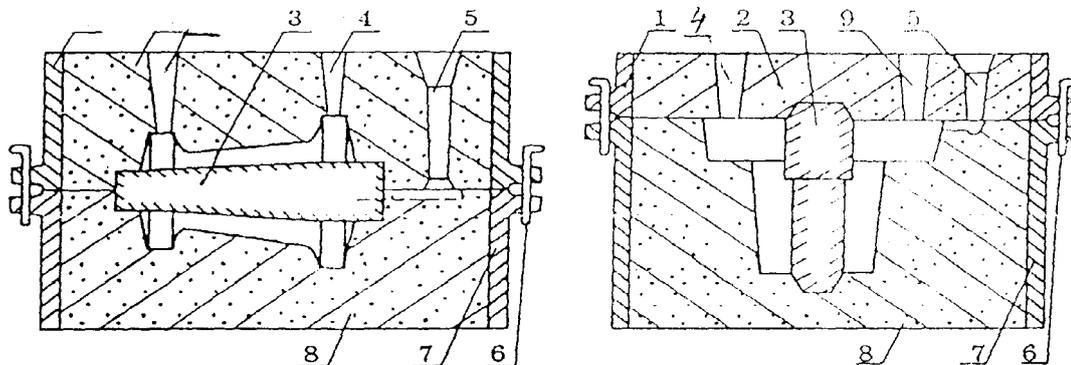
Эскизы литейных форм в сборе: 1-верхняя опока; 2-верхняя полуформа; 3-стержень; 4-выпор; 5-стояк; 6-штырь; 7-нижняя опока; 8-нижняя полуформа; 9-прибыль.
